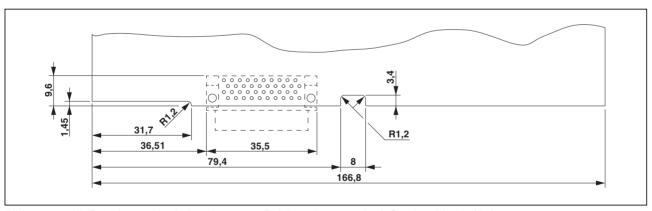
Maßzeichnung der Leiterplatte vom Gehäuse (2201500) mit Steckverbinder (B2)
